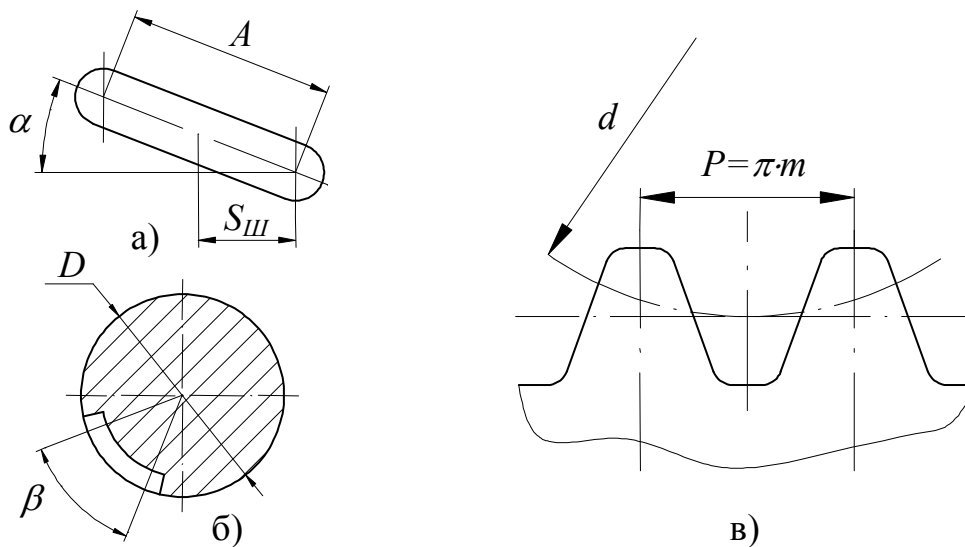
Розрахункова схема РГ байонетний паз – зубчаста рейка: а) розгортка байонетного пазу; б) переріз оправки з байонетним пазом; в) схема зубчастої передачі шестерня-рейка
